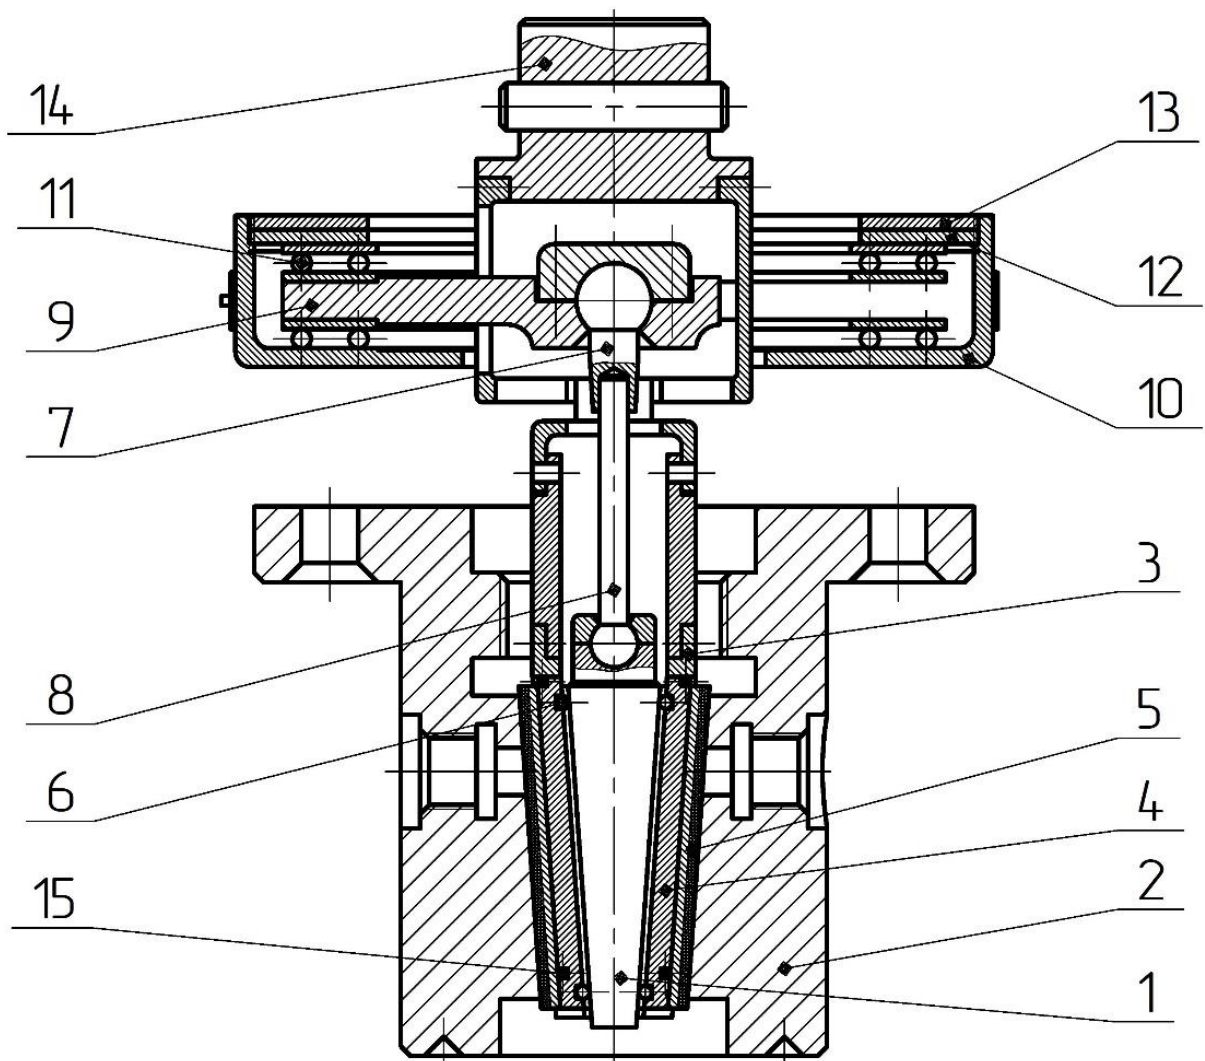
Хонінгувальна головка для обробки конічного отвору корпусу:
